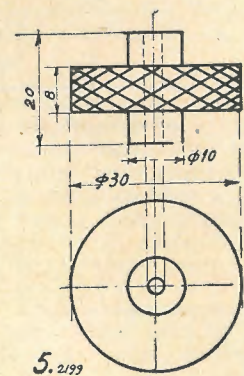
Dimensioni dell'avvolgimento e del supporto della bobina di impedenza Z.
